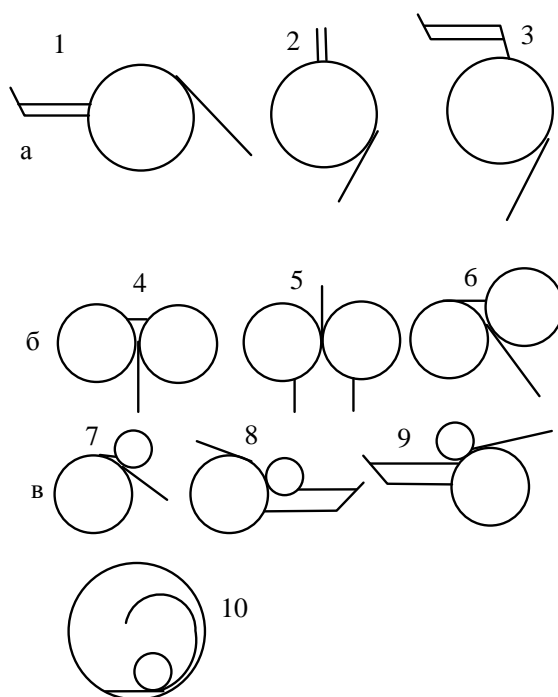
Принципиальные схемы валковых установок непрерывной отливки полосы: а – одновалковые с переливом (1), вытягиванием (2) и подачей по желобу жидкого металла (3); б – с двумя валками одинакового диаметра и подачей металла сверху (4), снизу вверх (5), по диагонали (6); в – с двумя валками разного диаметра, их тангенциальным расположением и внешней (7 – 9) или внутренней (10) подачей металла
